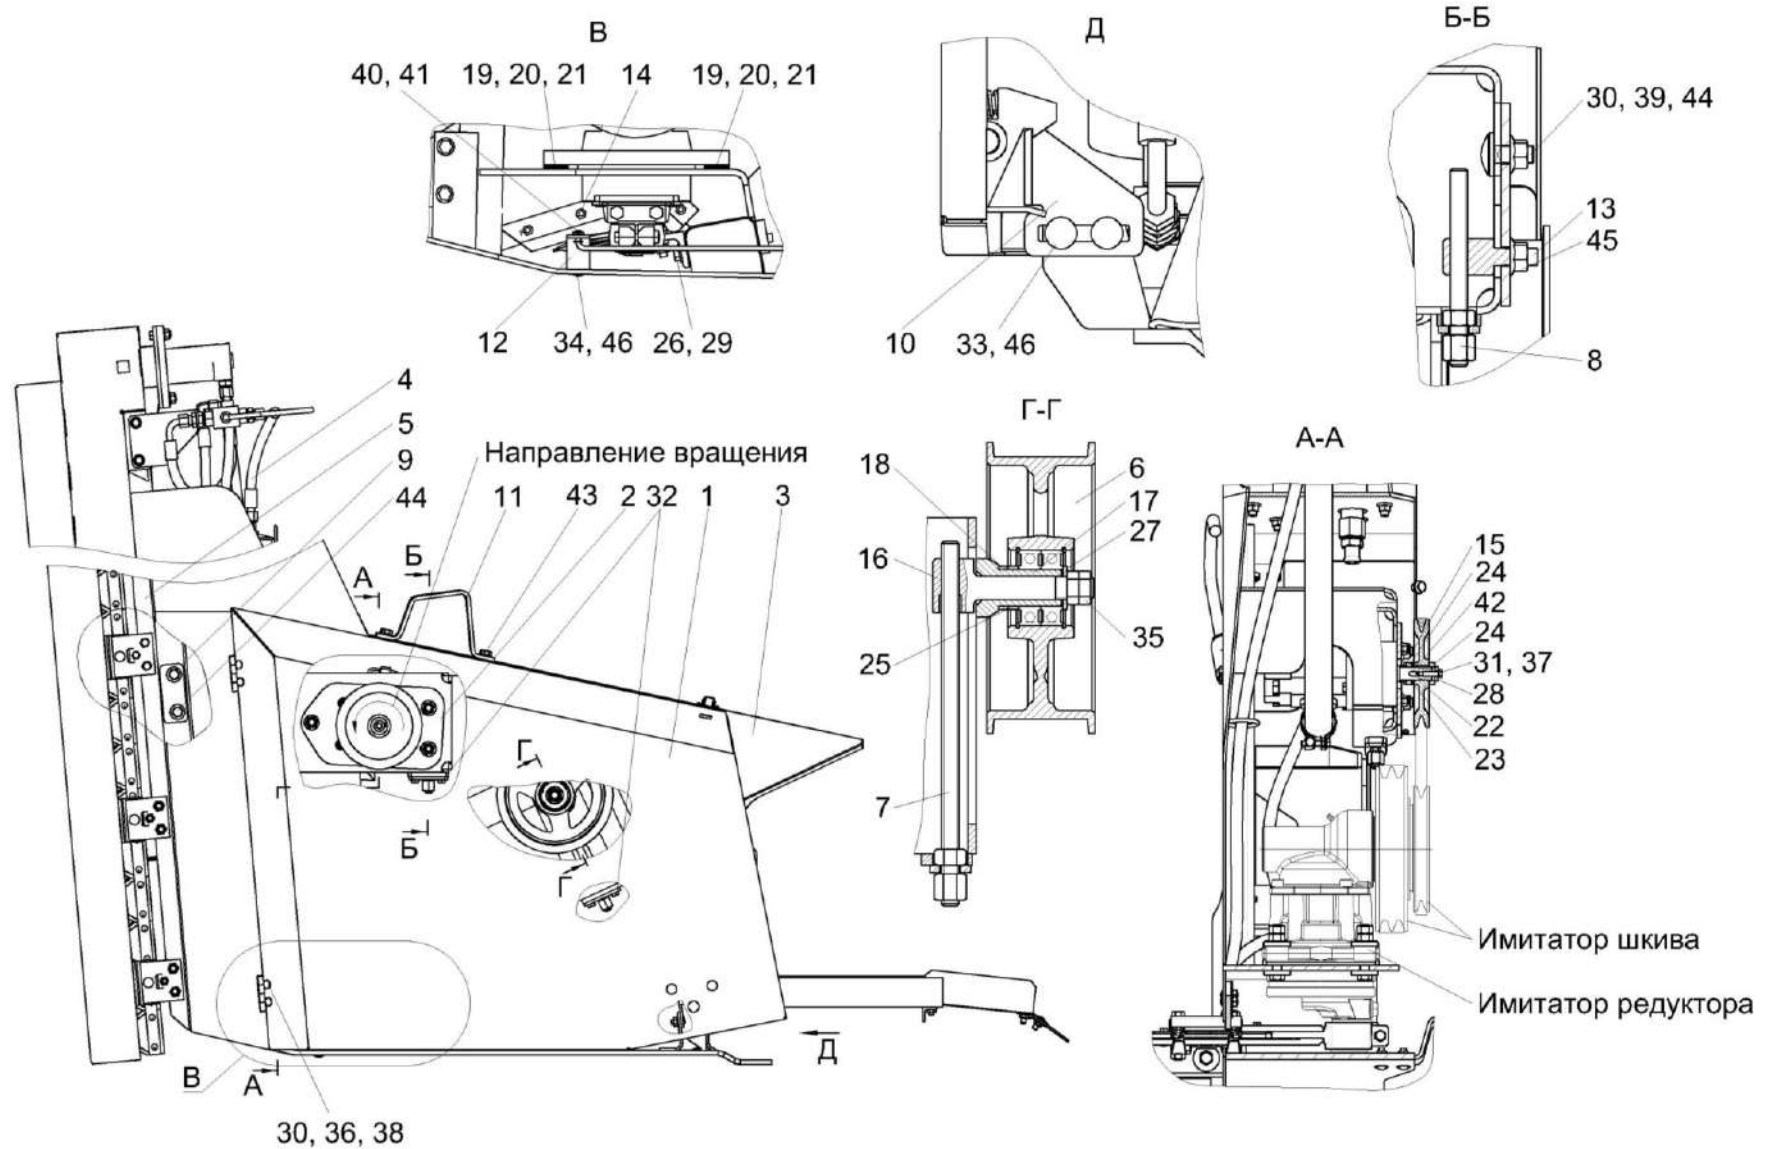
Приспособление для уборки рапса КЗК 2540000А (лист 2)
